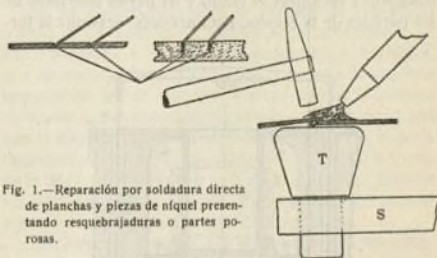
Reparación por soldadura directa de planchas y piezas de níquel presentando resquebrajaduras o partes porosas.
